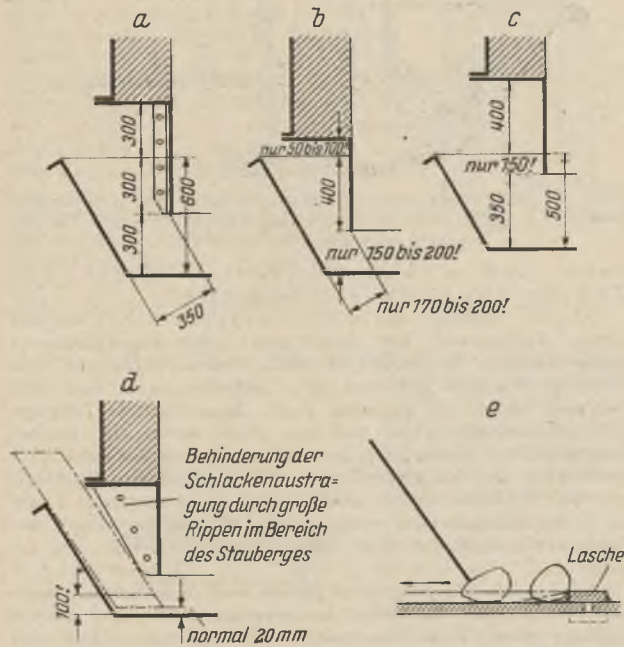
Richtige (a) und falsche (b bis e) Ausführung des Gaserzeuger-Unterteils in Bezug auf die Schlackenbewegung und den ausnutzbaren Winddruck.
